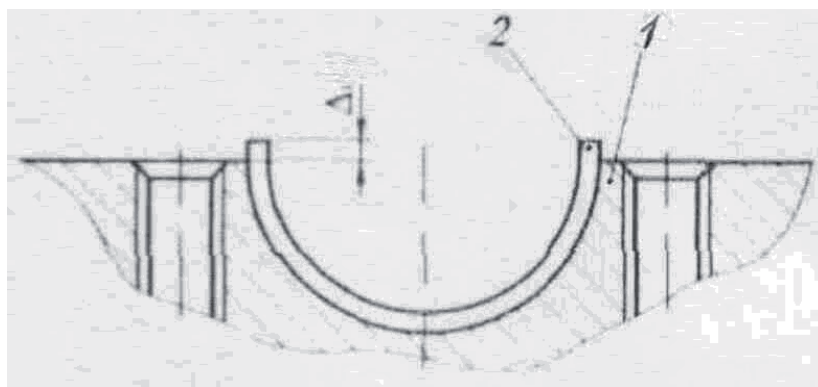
Расположение вкладыша в корпусе подшипника при монтаже: 1 – корпус; 2 – вкладыш
